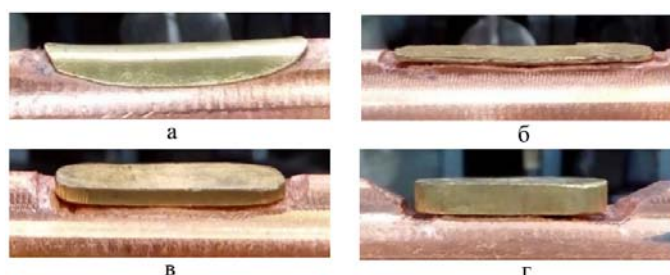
Искусственные дефекты из сплава Л63 в литой заготовке
